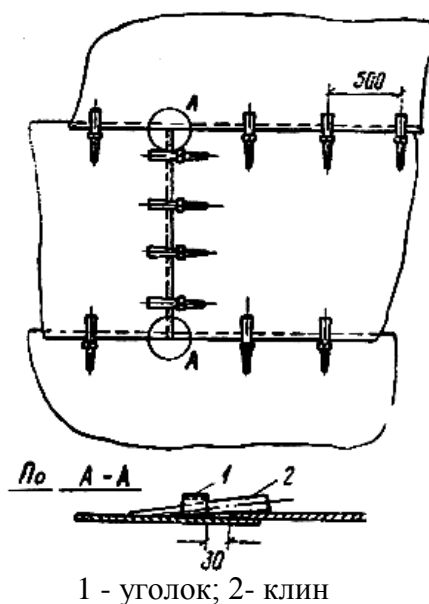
Применение стяжных клиновых приспособлений при сборке днища вертикального резервуара [10]
